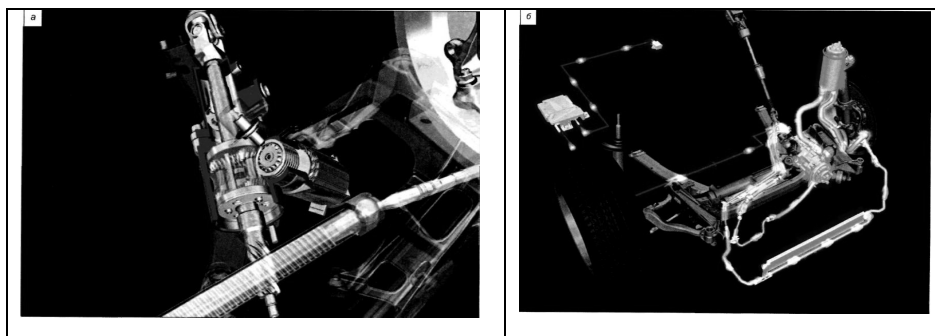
Система AFS: а — рулевой механизм; б — общий вид
